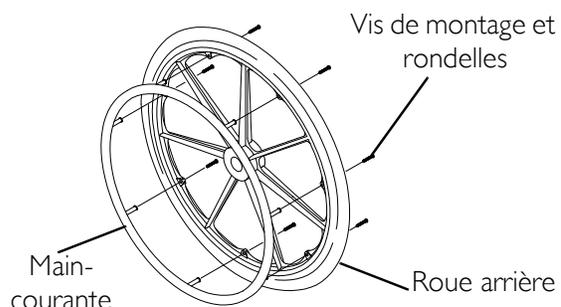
Remplacement des mains-courantes sans projection - Roues arrière composites
